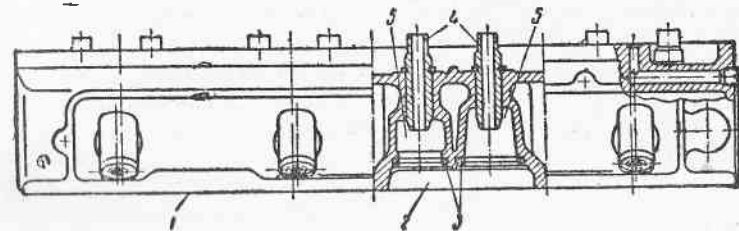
Головка цилиндров верхнеклапанного двигателя автомобиля М-21 «Волга»:
